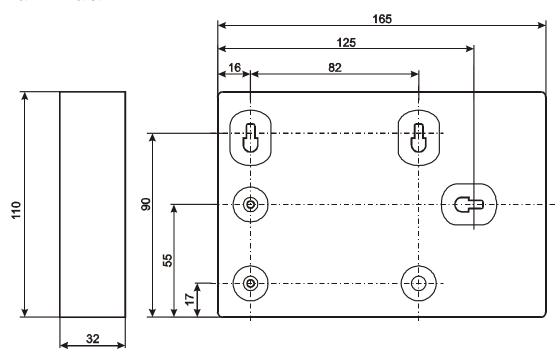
Внешний вид и габаритные размеры БРЛ в исп. IP20
